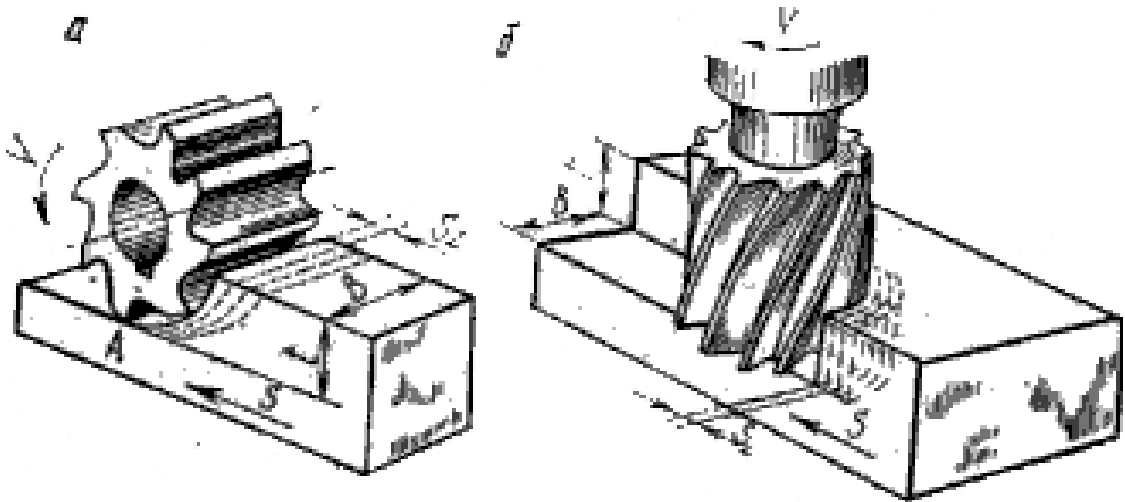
Види фрезерування: *a* – циліндричне; *b* – торцеве
